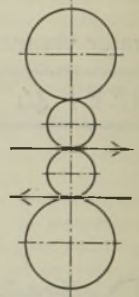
Walzvorgang beim Vierwalzengerüst.
